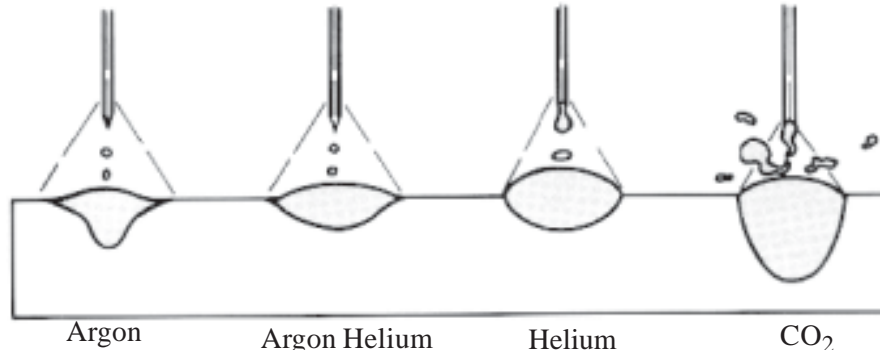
Contorno e penetração da solda para diversos gases de proteção.
